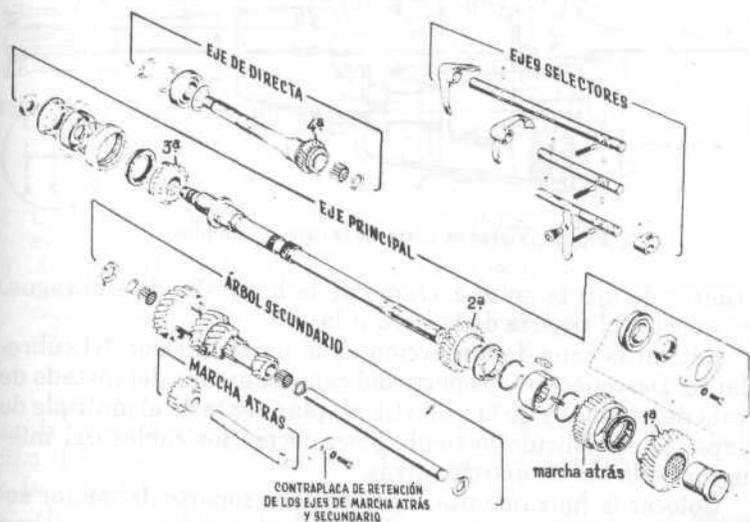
Disposición de los ejes selectores y del tren de engranajes.
